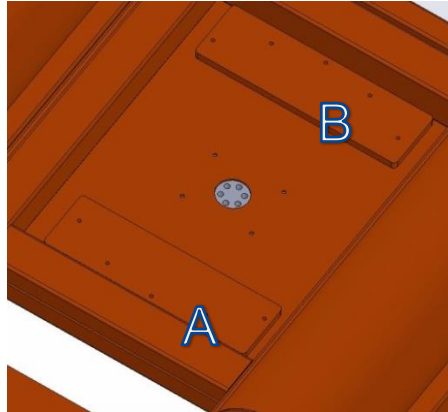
Vista superior de la mesa empaquetadora, las placas A y B ayudan a la fijación del aro giratorio.
